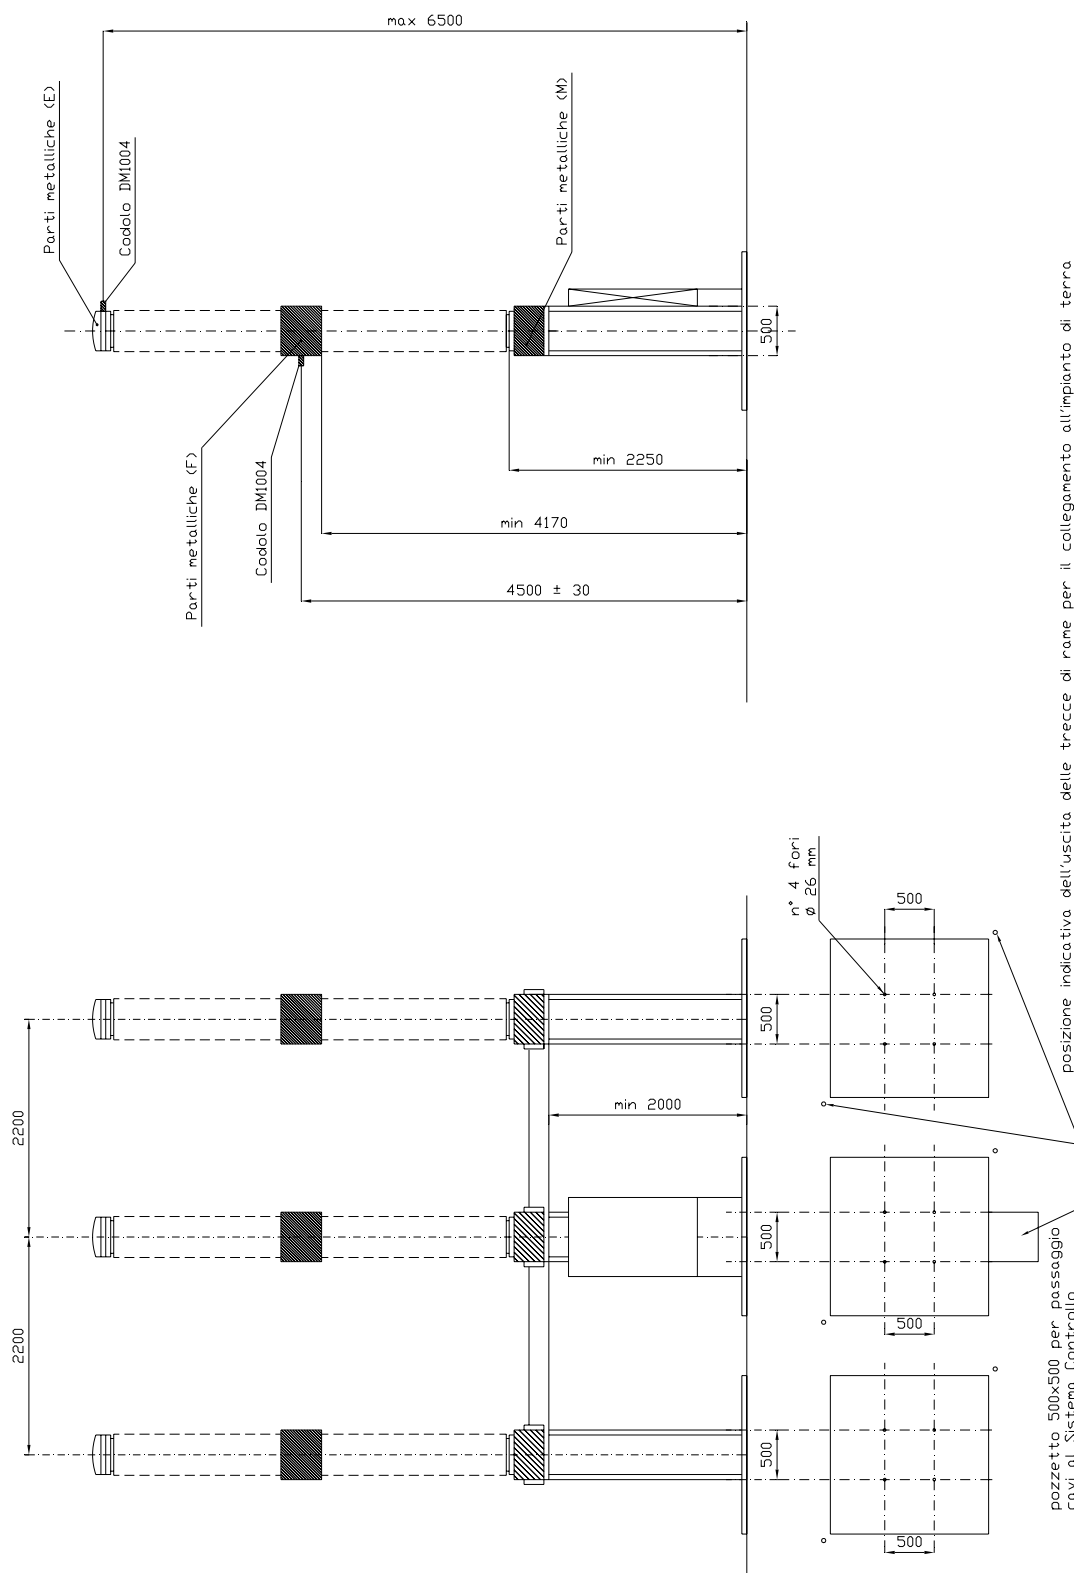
Dimensioni principali degli interruttori con TA incorporato
